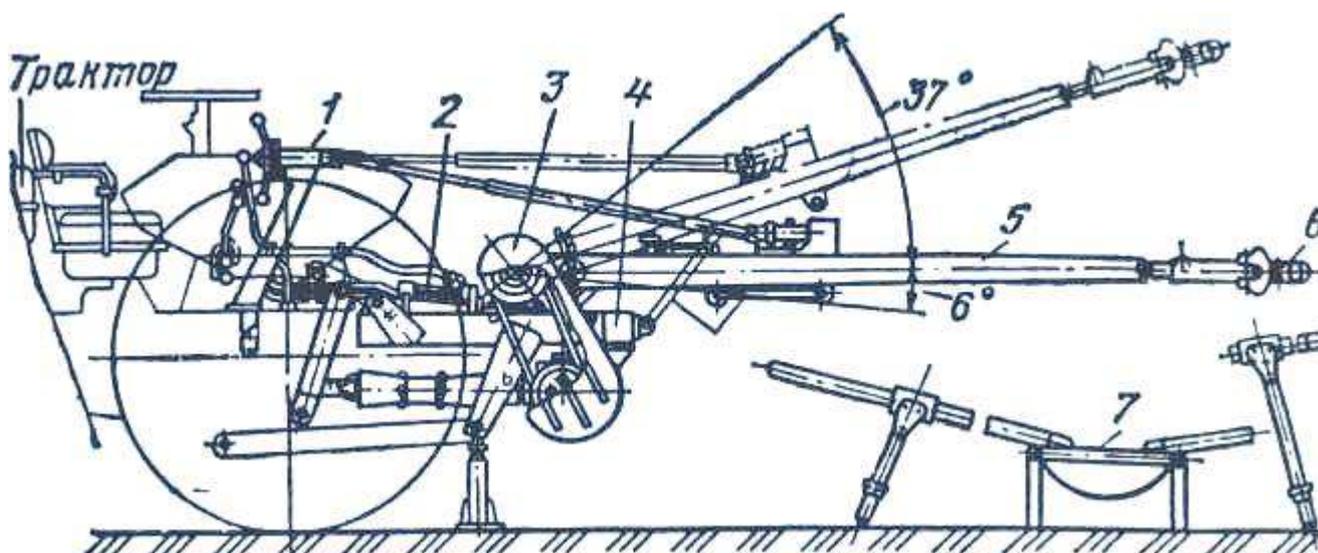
Плодоуборочная машина ВСО-25 «Стрела» с улавливающим приспособлением УП-5; 1 – механизм поворота захвата вокруг своей оси; 2 – механизм подъема и опускания стрелы; 3 – вибратор; 4 – рама вибратора; 5 – стрела; 6 – хват; 7 – улавливающее приспособление
